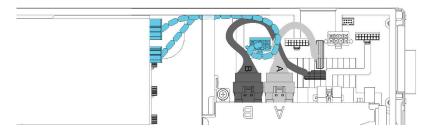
Roteamento do PCIe#1-A, PCIe#2-B e do cabo de energia auxiliar da placa riser frontal
